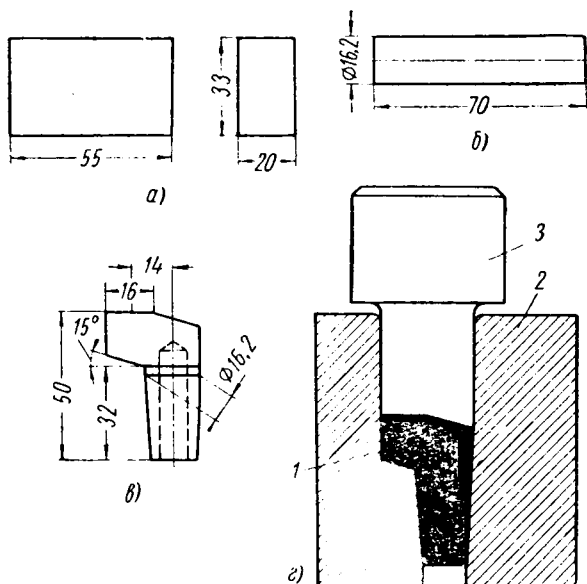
Схема штампа и заготовка металла для изготовления электрода методом прямого выдавливания:
